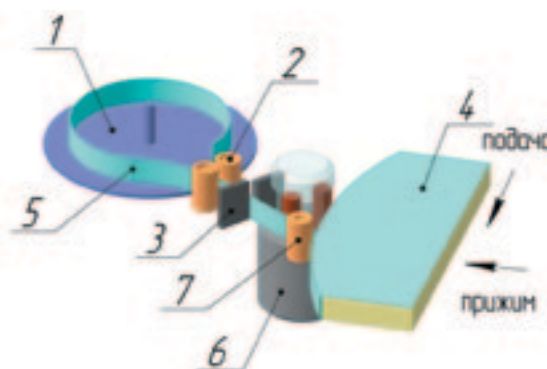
Базовый модуль: 1 – магазин; 2 – ролики подачи; 3 – гильотина; 4 – деталь; 5 – лента облицовочного материала; 6 – клеевая ванночка; 7 – опорный ролик
